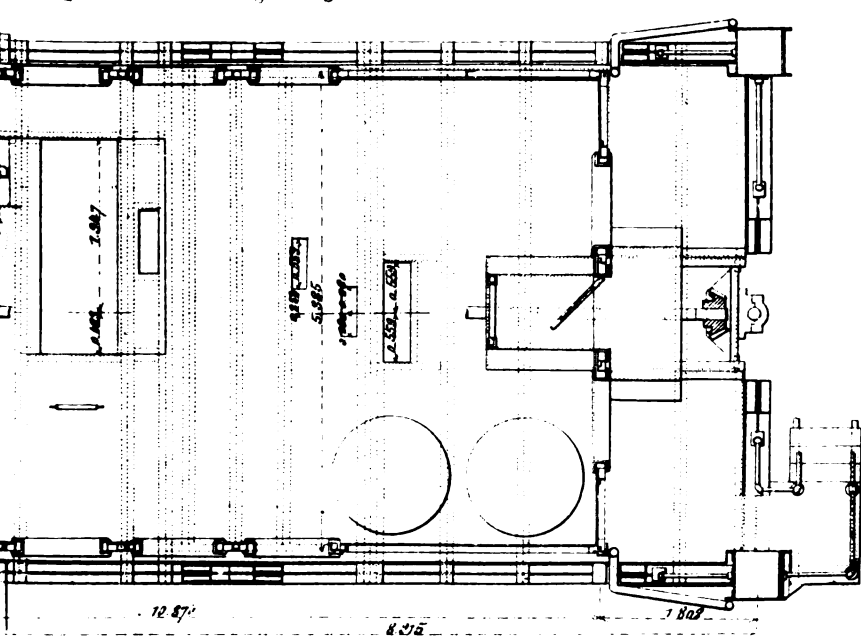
et 7. Plan et Coupe du tambour tournant.
